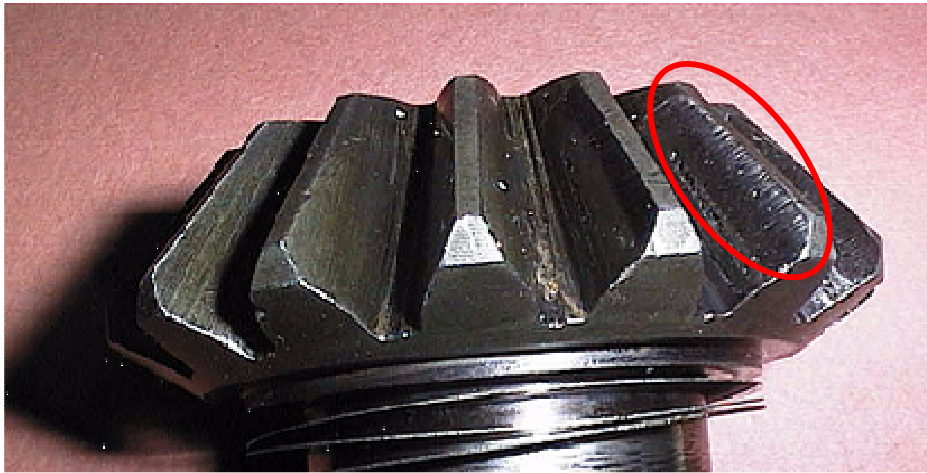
Engranaje con scoring destructivo. Pruebas realizadas en John Deere Ibérica.
